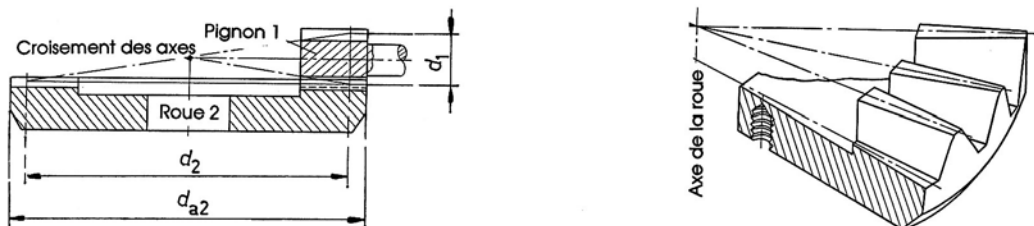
Engrenage de champ : disposition des roues et forme de la denture sur la roue de champ
